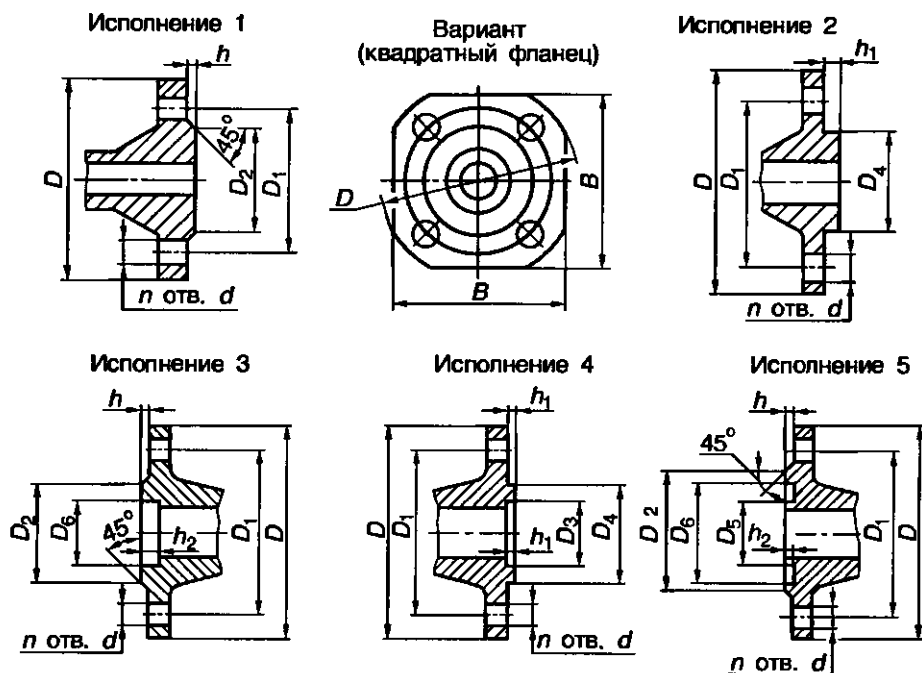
Фланцы исполнений: 1 – с соединительным выступом; 2 – с выступом; 3 – с впадиной; 4 – с шипом; 5 – с пазом
